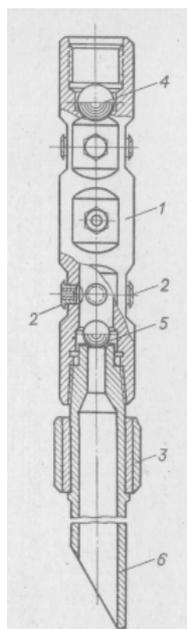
Гидропескоструйный перфоратор: 1 – корпус перфоратора; 2 – насадки (сопла истечения жидкости); 3 – центратор; 4 – шар опрессовочного клапана; 5 – шар клапана; 6 – хвостовик
